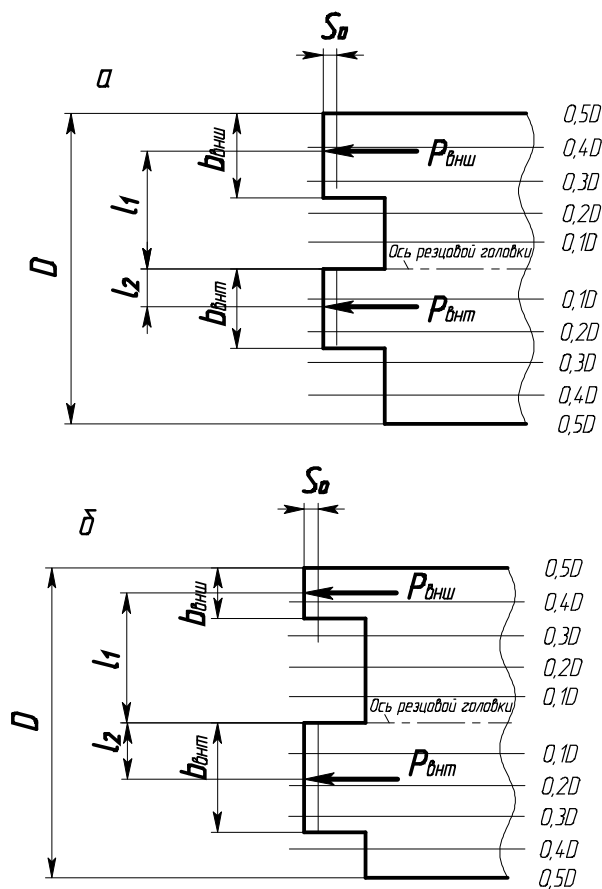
Схема режущей части резцовой головки и действующих сил и моментов резцовой головки: а – с неуравновешенными силами при равенстве ширины ассимет-
